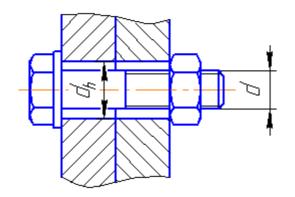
Конструктивный зазор между стержнем болта и отверстием в деталях
